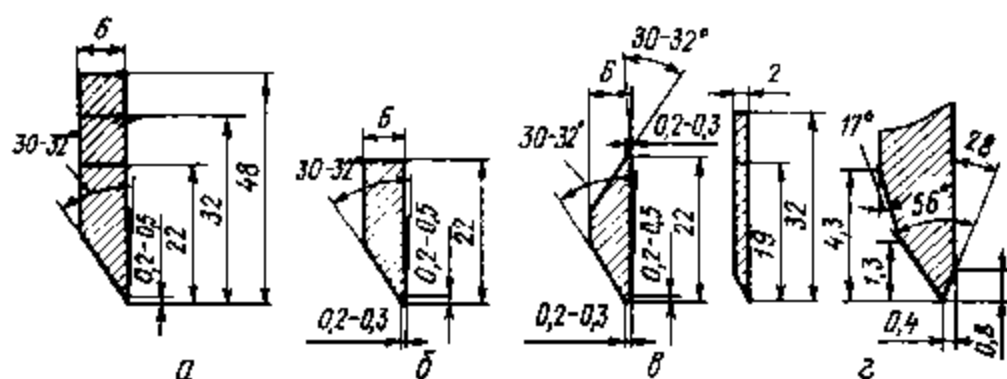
Профили режущих кромок резак для вырубания деталей верха обуви
